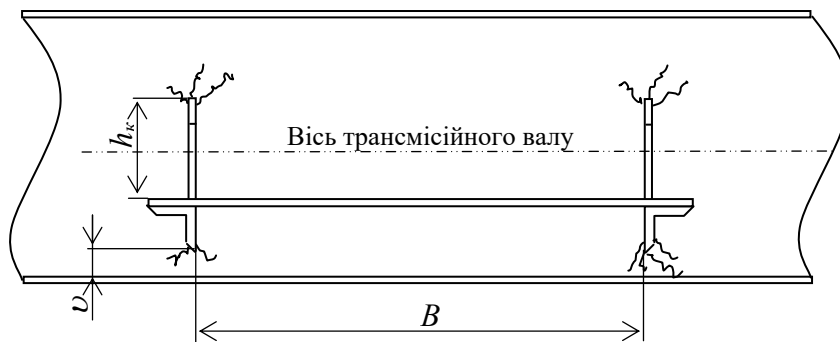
Деталізація пошкоджень поз.1, (рис.1) стінки мостової балки (привод механізму пересування крану умовно не наведений): v – відстань від нижнього поясу до місця кріплення поперечного опорного куточка площадки механізму пересування; h_k – висота підсилюючої косинки; B – відстань між опорними куточками
